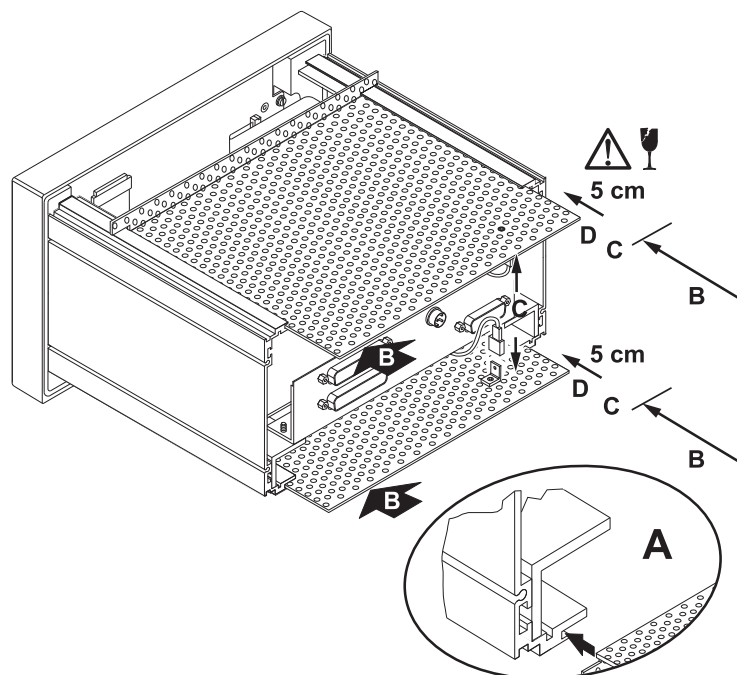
Einschieben der Lochbleche und Befestigung der Massekabel
